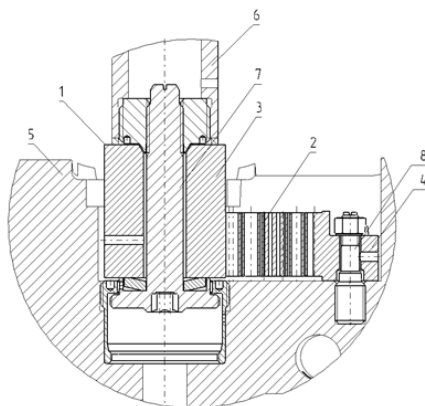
Сборка ЭС, 2 – токоведущие ламели, 3 – центральный фланец, 4 – боковой фланец, 5 – модуль blankets, 6 – пьедестал ВК, 7 – центральный болт, 8 – шпильки
